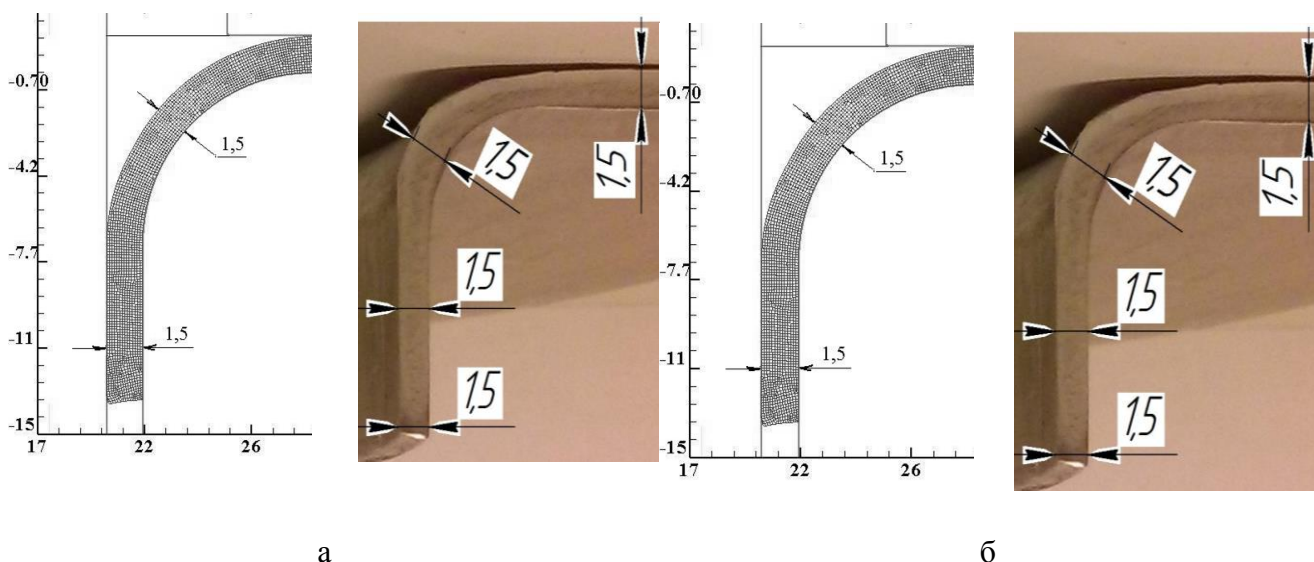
Розрахункові по МСЕ та експериментальні форма і розміри в міліметрах zdeформованих частин: а – традиційної заготовки; б – зпрофільованої заготовки
